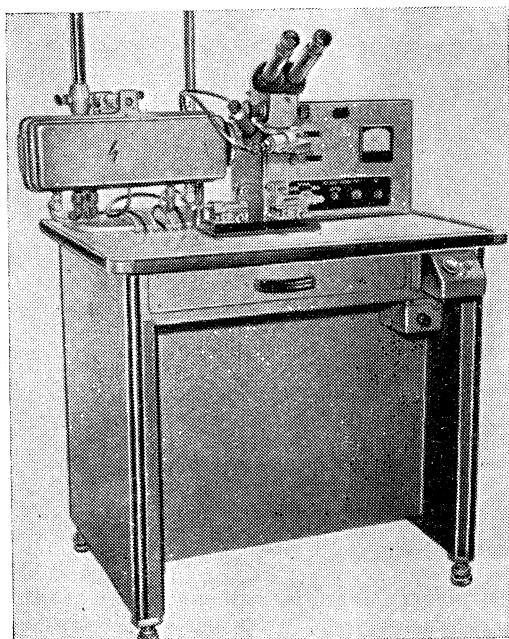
Сварочная лазерная установка СУ-1.
